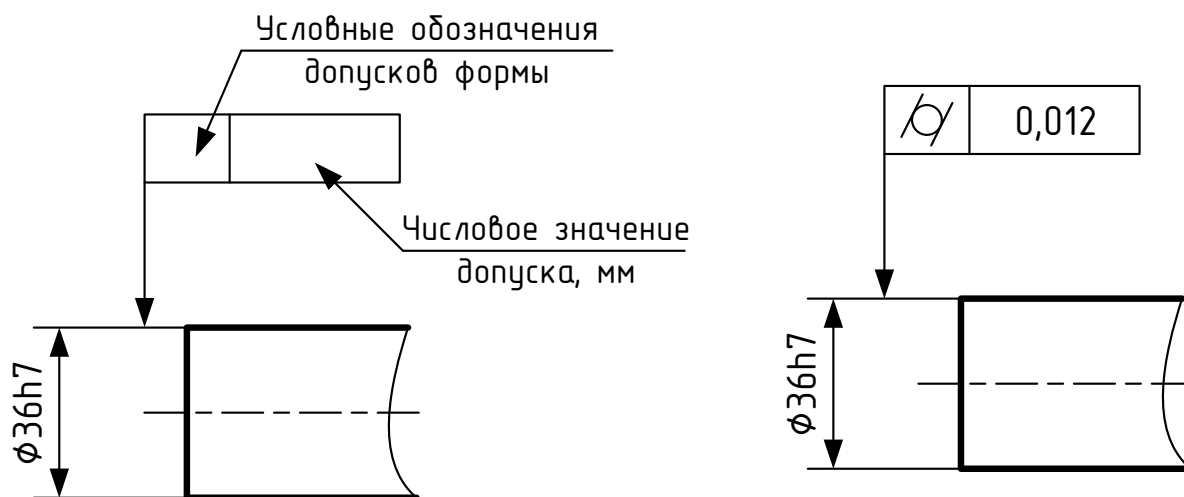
Условные обозначения допусков формы
